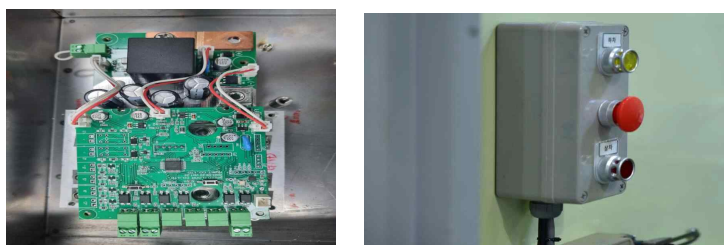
제어부 PCB 판넬 및 비상정지 버튼
